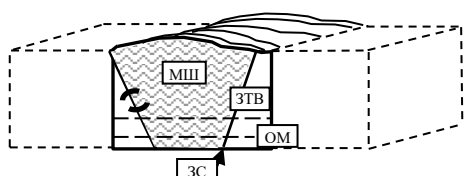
Общий вид сварного соединения и схема вырезки металла для изготовления фольг для ПЭМ.
